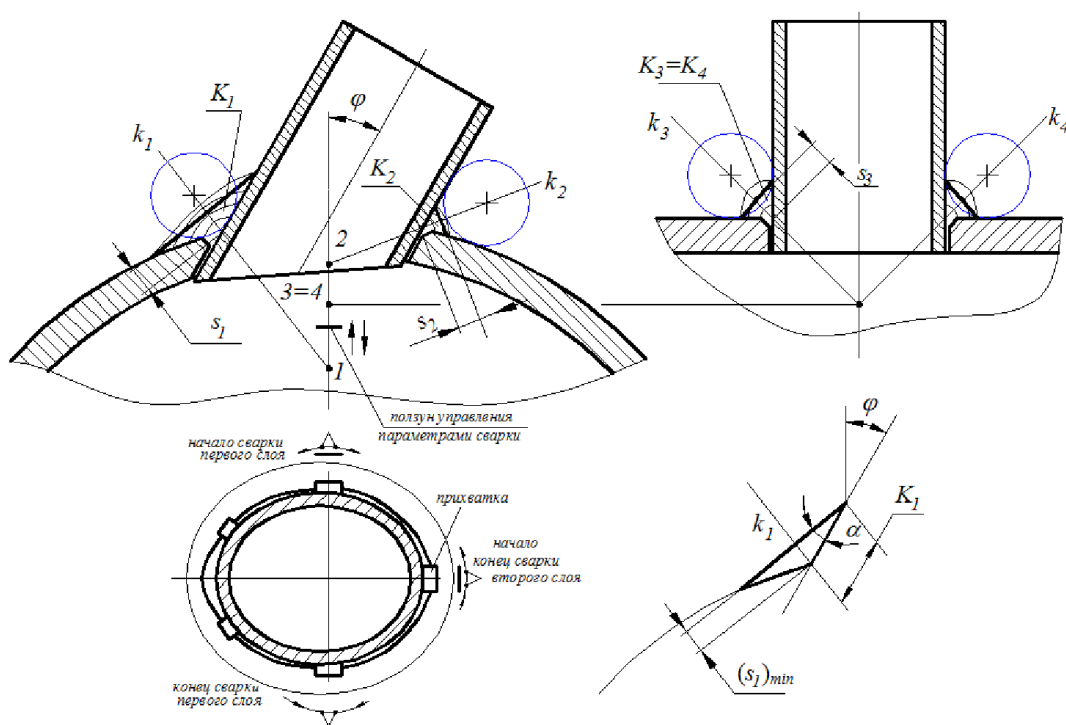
Схема формирования сварного шва в ходе приварки штуцера к обечайке сосуда
